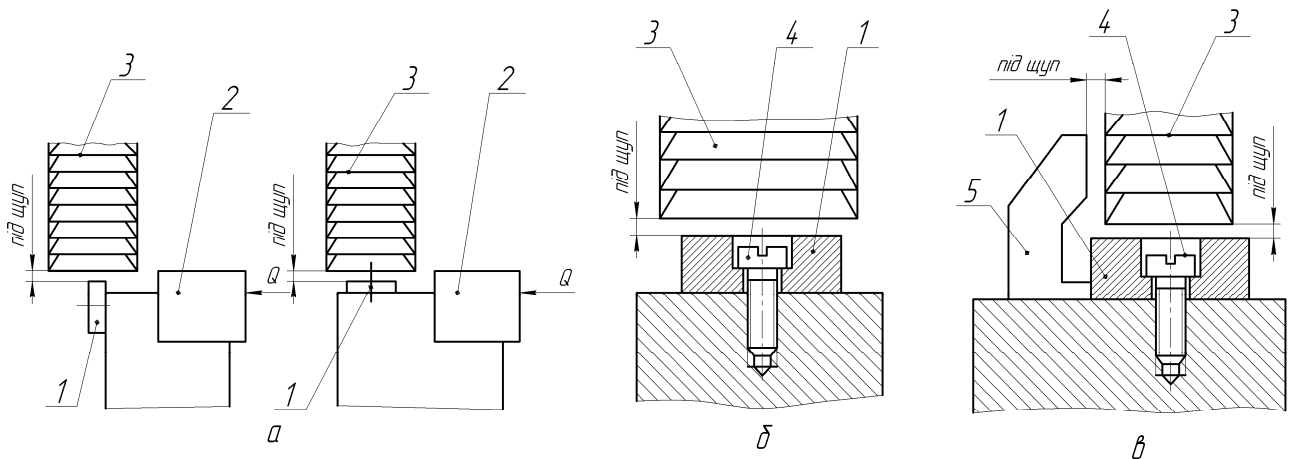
Схеми й розрізи засобів налагодження фрезерних верстатів: а – налагодження фрез на певний розмір; б – для руху фрези в одному напрямку; в – для руху фрези у двох напрямках; 1 – пристрій 2 – деталь, 3 – фреза, 4 – гвинт, 5 – косинець
